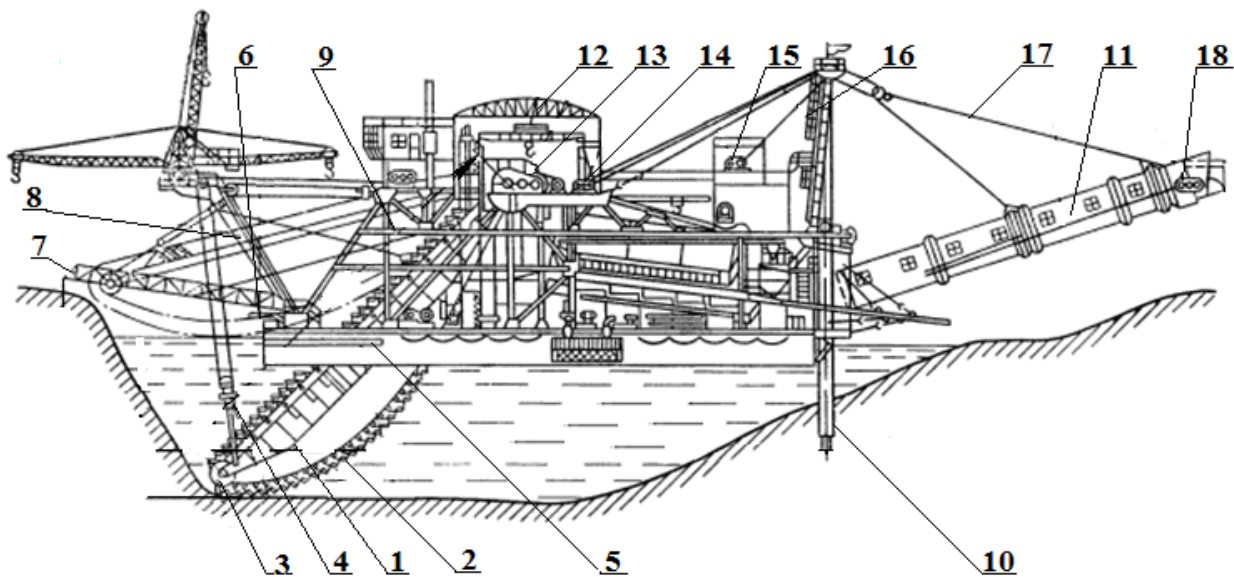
Конструктивна схема багаточерпакової драги: 1 – черпакова рама; 2 – черпаковий ланцюг; 3 – нижній черпаковий барабан; 4 – підвіс черпакової рами; 5 – понтон; 6 – носовий гідромонітор; 7 – береговий місток; 8 – передня щогла; 9 – суперструктура; 10 – паля; 11 – відвалоутворювач (стакер); 12 – мостовий кран; 13 – головний привід черпакового ланцюга); 14 – лебідка; 15 – лебідка підняття стакера; 16 – задня щогла; 17 – підвіс стакера; 18 – привід конвеєра стакера
